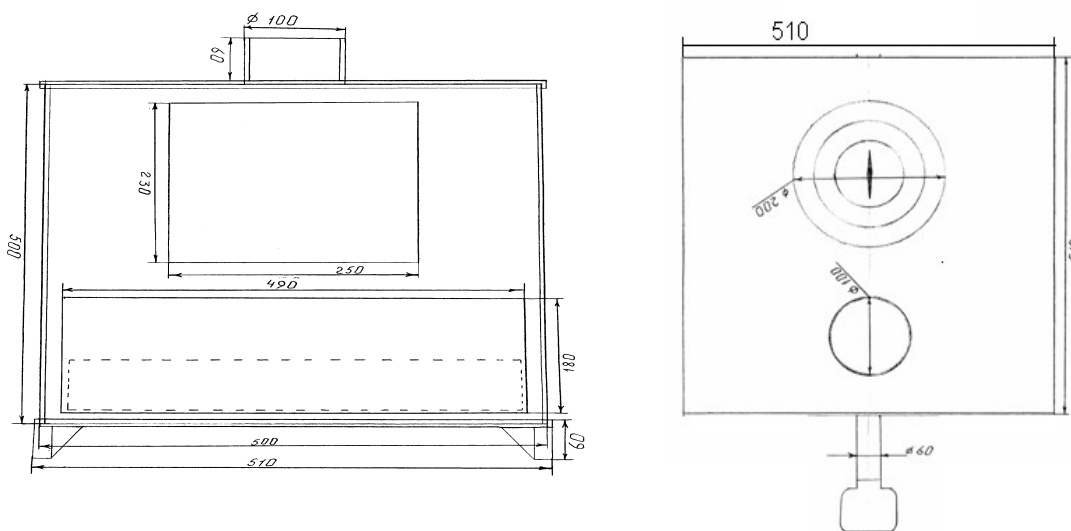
Габаритные размеры печи (вид сбоку и сверху)
